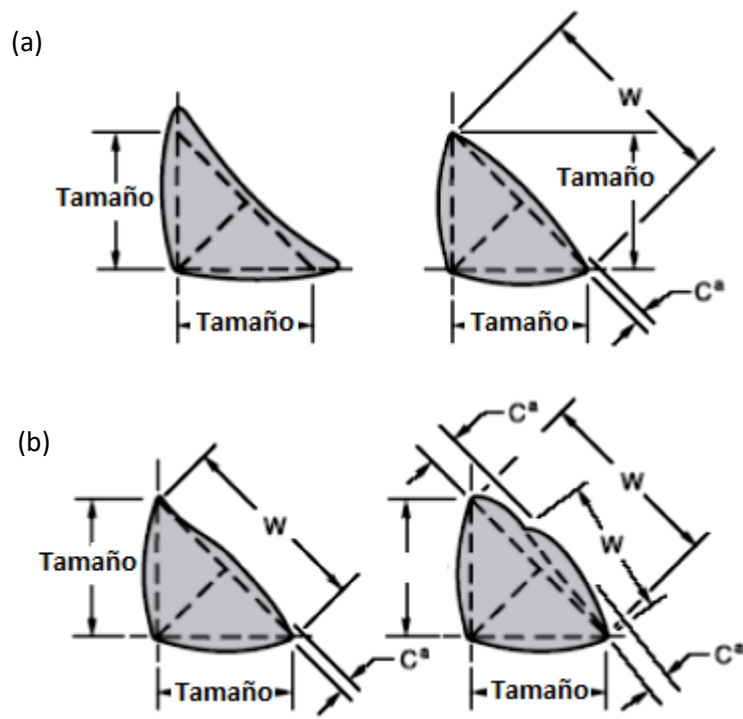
Perfiles de soldadura de filete. (a) Deseables y (b) Aceptables [4].
